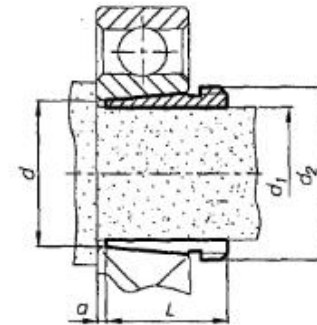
Закрепление внутреннего кольца подшипника на валу с использованием стяжной втулки
